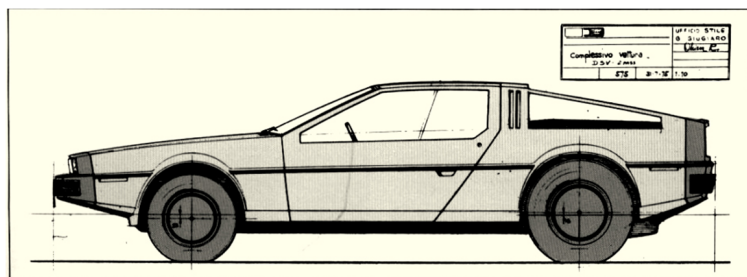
Чертеж внешнего вида DMC-12, разработанный Д. Джуджаро
